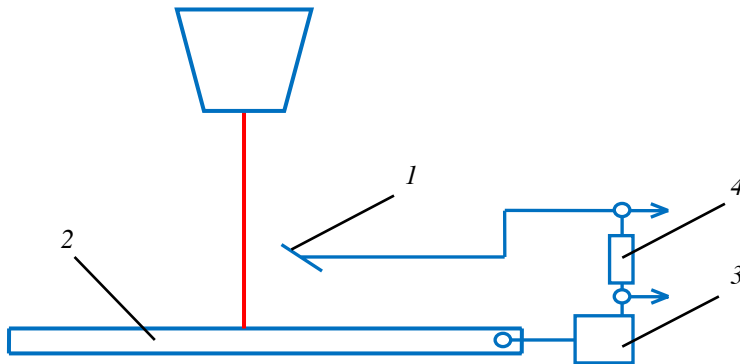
Схема регистрации вторично-эмиссионного тока при лазерной сварке: 1 – коллектор заряженных частиц; 2 – свариваемое изделие; 3 – источник напряжения смещения; 4 – резистор нагрузки
